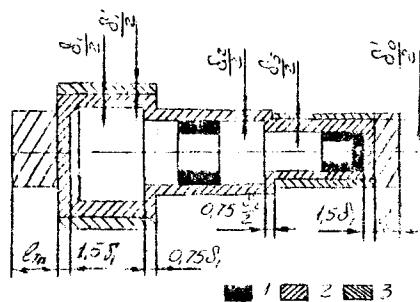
Эскиз детали с напусками (1), основными (2) и дополнительными (3) припусками
